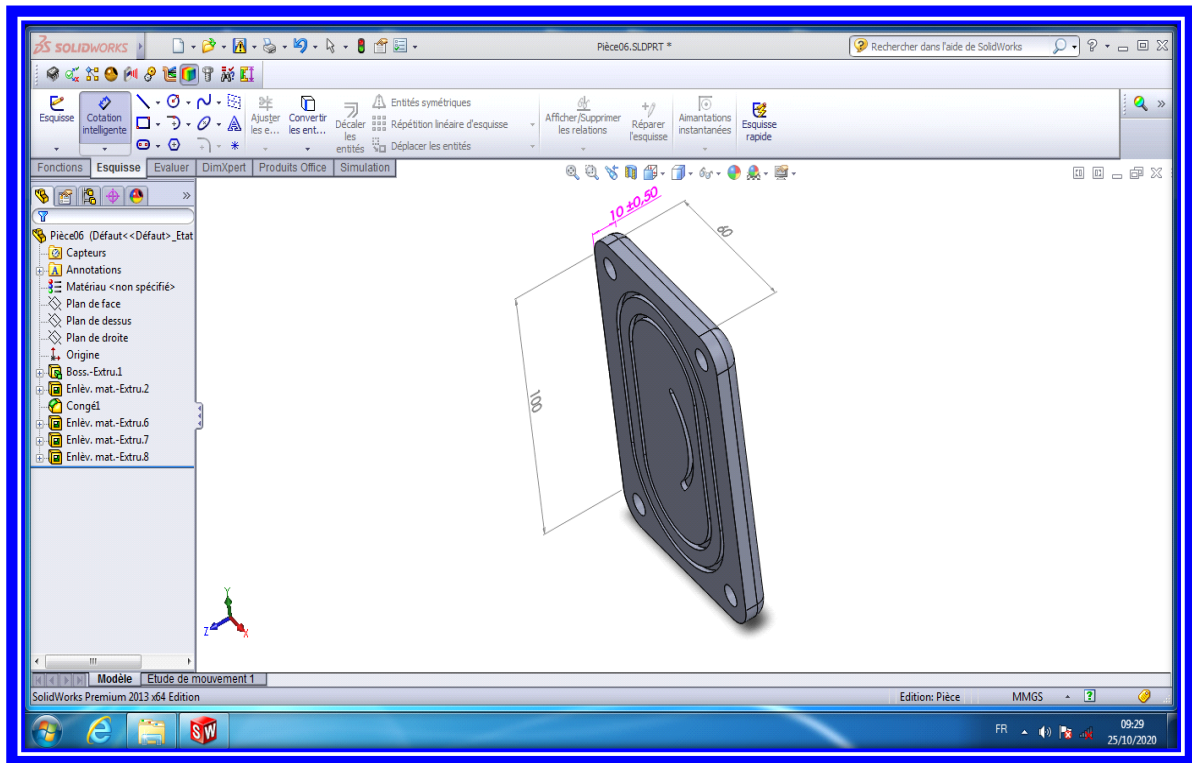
Interface graphique du couvercle arrière de la pompe sous-SolidWorks
